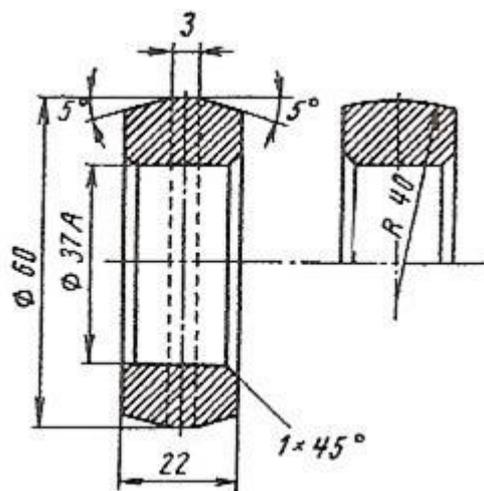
Ролики для обкатывания цилиндрической поверхности
